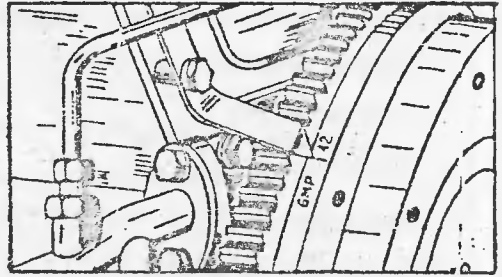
б. Метка на маховике установки поршня первого и шестого цилиндров в верхней мертвой точке 12-тицилиндрового двигателя.
